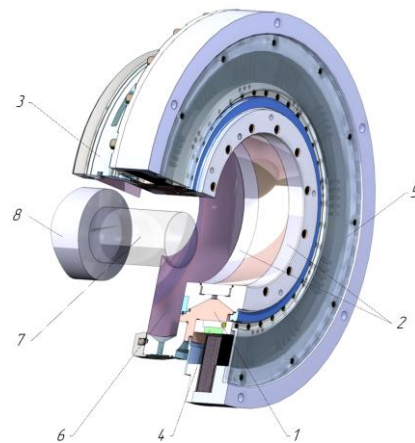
Тривимірна модель шпиндельного вузла верстата “Алмаз – 150 ЕШВ”: 1, 2 - рухома і нерухома частини конічної аеростатичної опори; 3 - натяжний пристрій для АКВР; 4, 5 - первинний і вторинний елементи електроприводу; 6 - ріжучий інструмент (АКВР 690 × 235); 7, 8 - монокристал, що розрізається, і його тримач відповідно.
